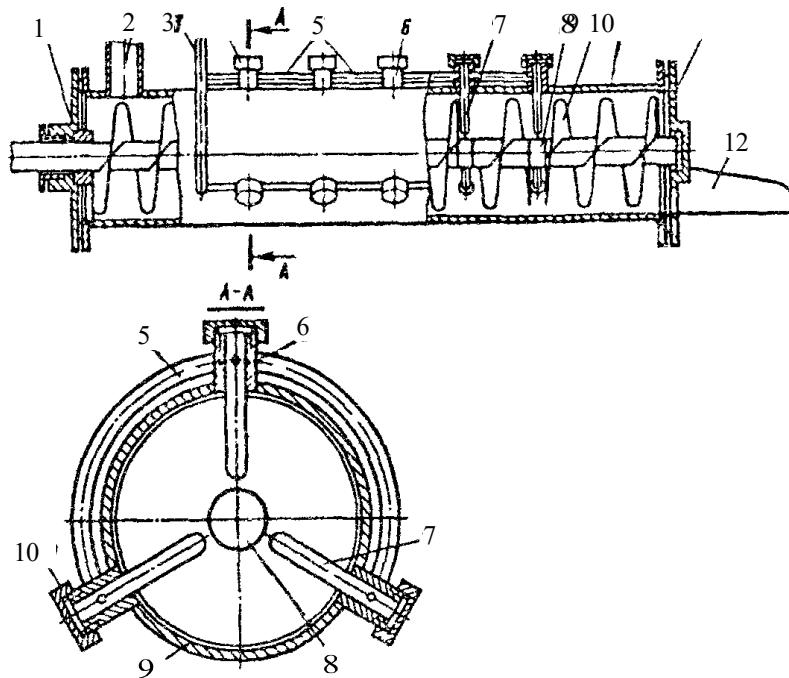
Термокоагулятор Я6-ФПК: 1 – задня кришка; 2, 3, 6 – патрубки; 4 – гайка; 5 – паровий колектор; 7 – вал; 8 – форсунка; 9 – шнек; 10 – корпус; 11 – передня кришка; 12 – лоток
